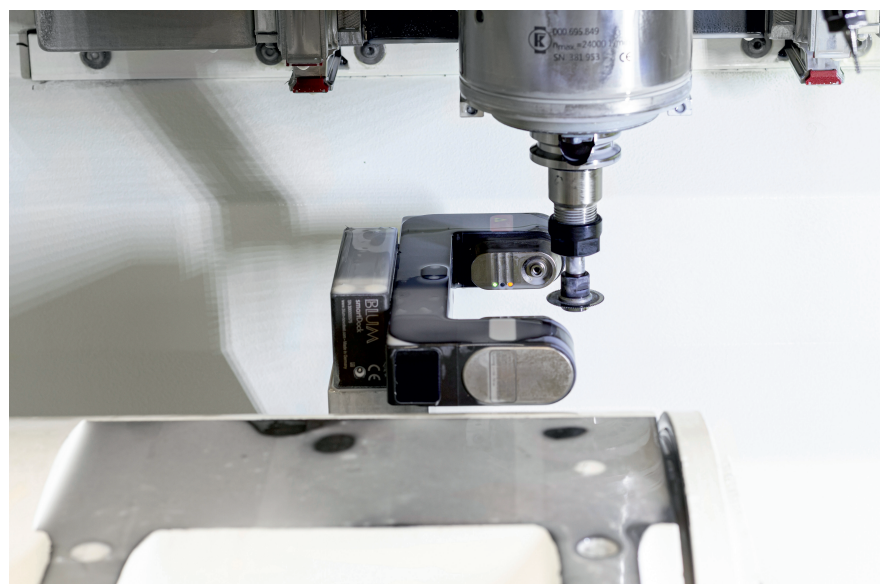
Lasermesssysteme von Blum vermessen und überwachen bei Stoffel Medizintechnik Werkzeuge mit wenigen Zehnteln im Durchmesser trotz Einsatz von Kühlmittel. © Blum-Novotest/Stoffel
